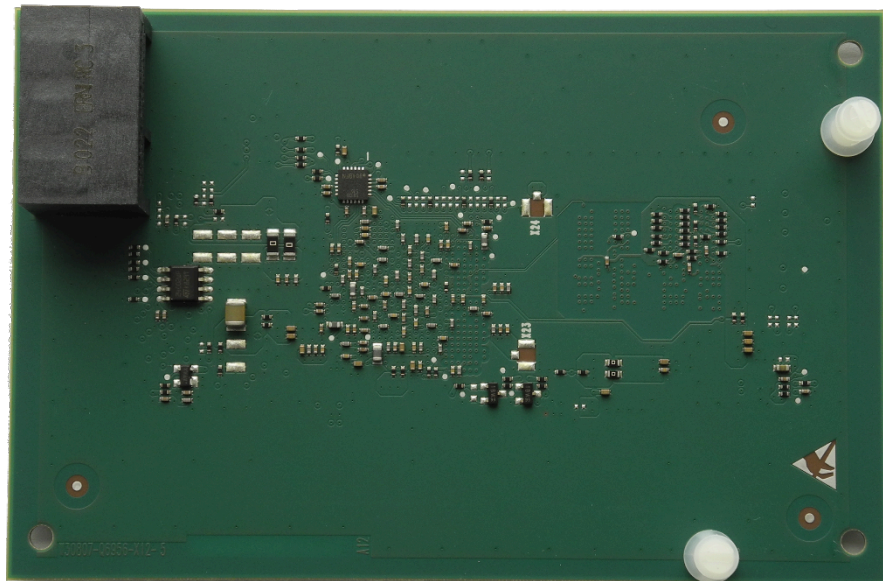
Exemple OCCBL - Face arrière avec boulons d'espacement insérés
